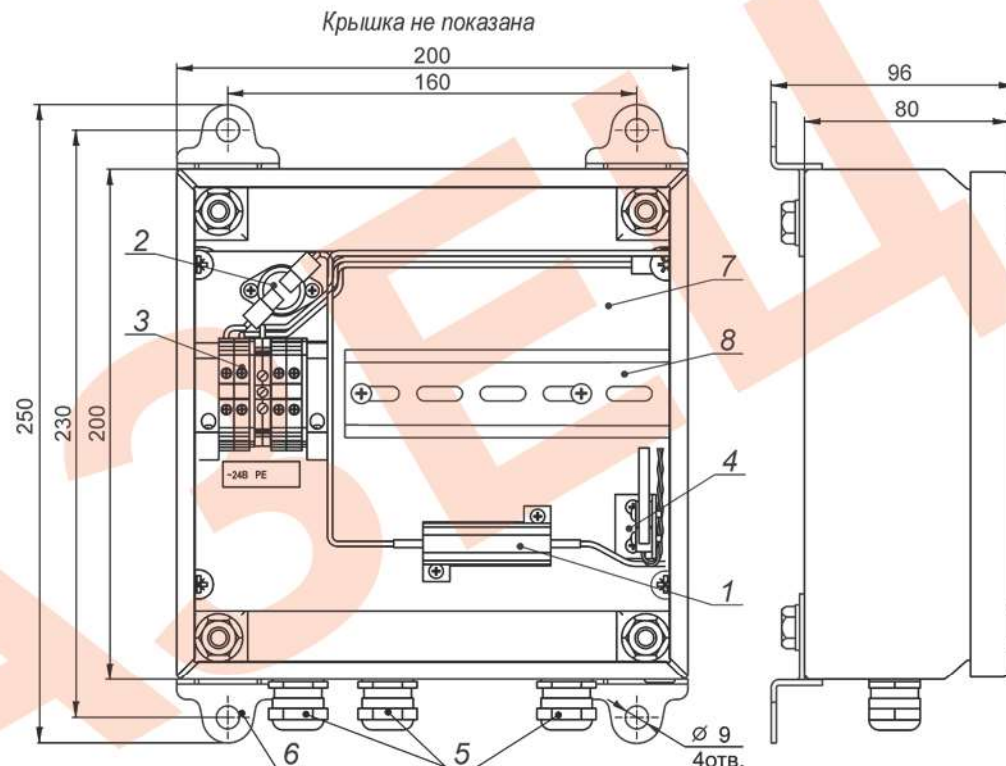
Устройство, габаритные и установочные размеры КМО-1
